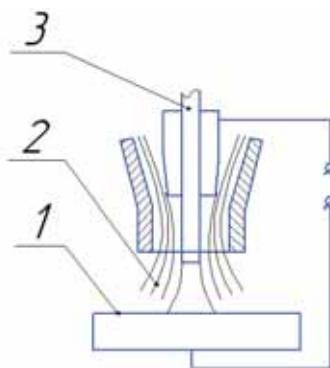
Сварка в защитном газе: 1 – деталь; 2 – защитный газ; 3 – электрод
